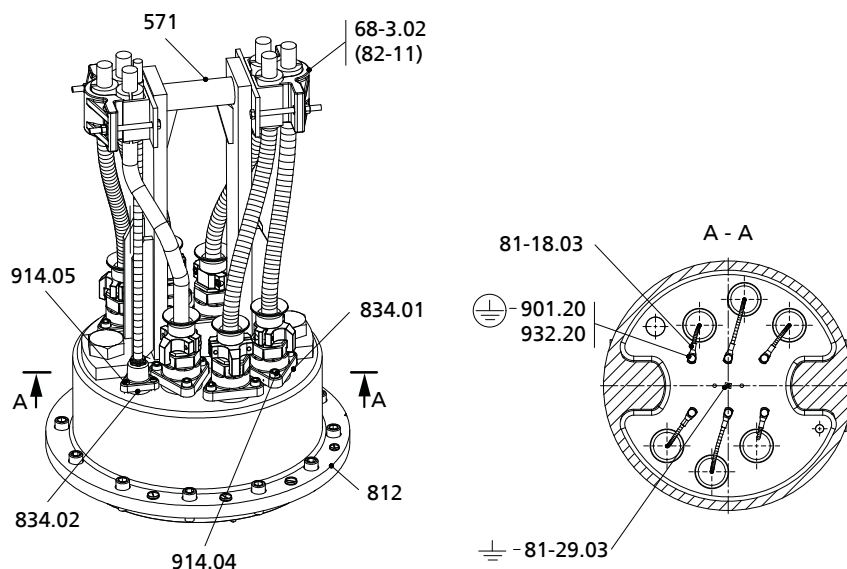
Демонтаж соединительного провода и кабельного ввода
